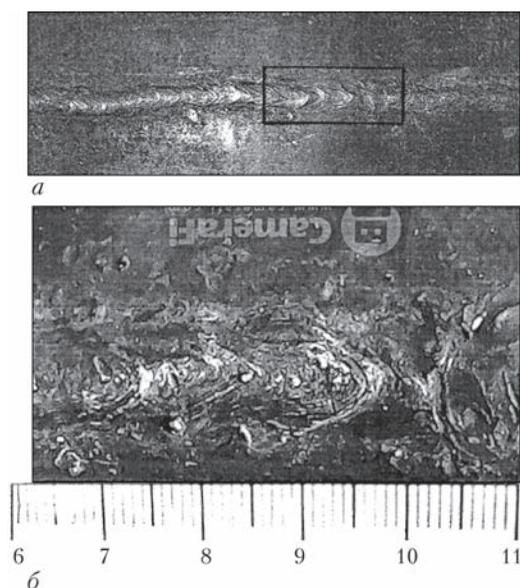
Пример записи изображения образца сварного шва (а) и его фрагмент (б) зоны возможного расположения внутренних дефектов с тремя поверхностными порами
